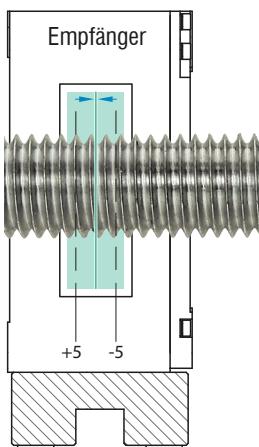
Schmale Messlinie für Messungen an steilen Kanten und Ecken, z. B. für Messungen an Gewindestangen
